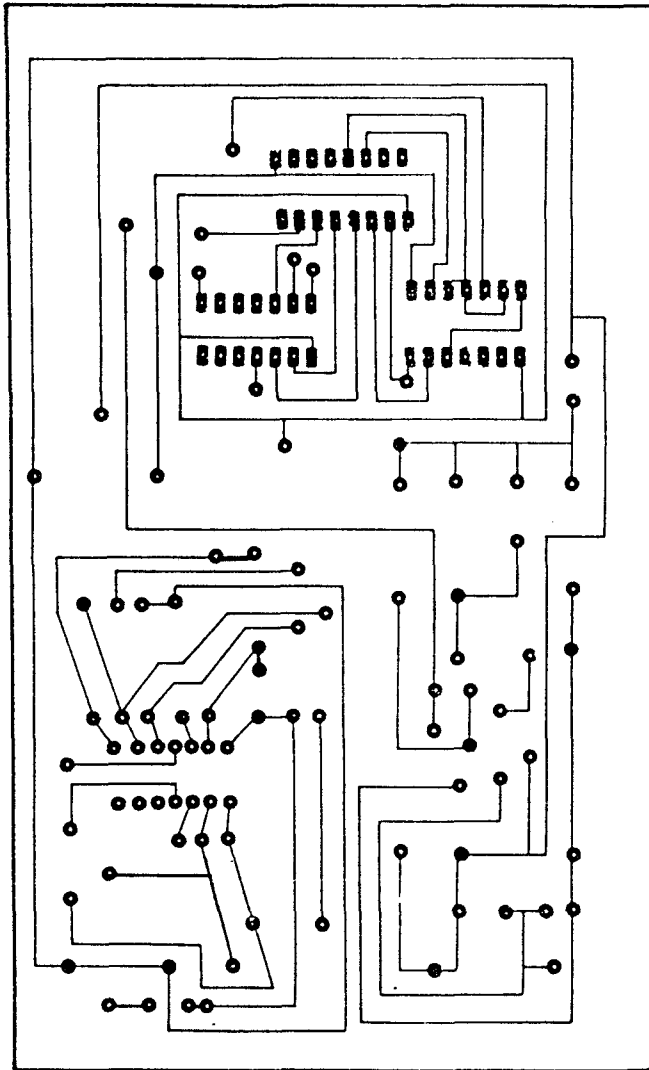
Dibujo de la placa de circuito impreso que fue diseñada para el oscilador de 3 KHz.
